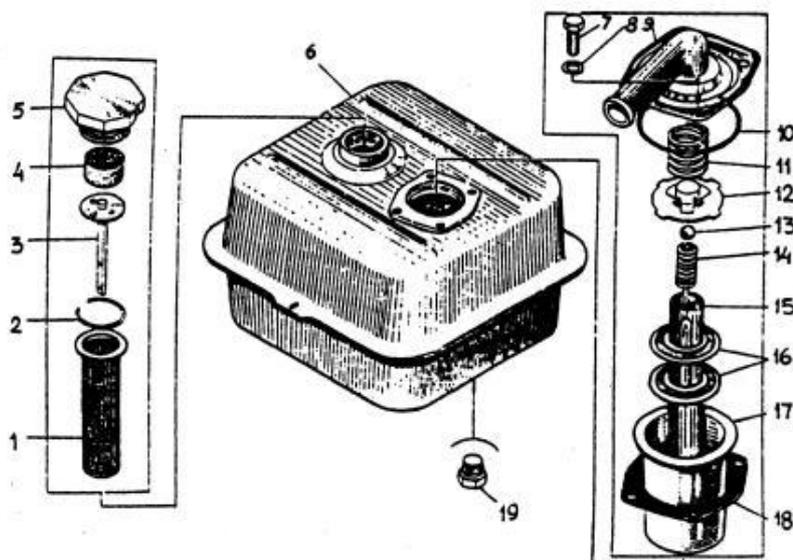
Масляный бак гидросистемы самосвала КамАЗ-5511: 1 — фильтр заливной горловины; 2 — кольцо стопорное; 3 — щуп; 4 — набивка волосяная; 5 — крышка заливной горловины; 6 — бак; 7 — болт; 8 — шайба пружинная; 9 — крышка фильтра; 10 — кольцо; 11, 14 — пружины; 12 — шайба отражательная; 13 — шарик; 15 — труба; 16 — элемент фильтрующий; 17 — корпус фильтра; 18 — прокладка; 19 — пробка
